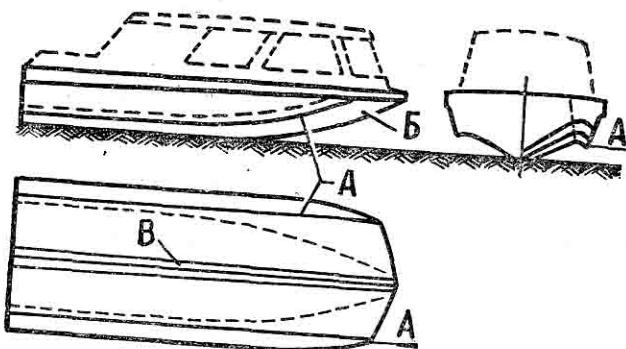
Корпус катера с обводами «кафедрал»: А — спонсоны, Б — центральная часть, В — килевая лыжа.
